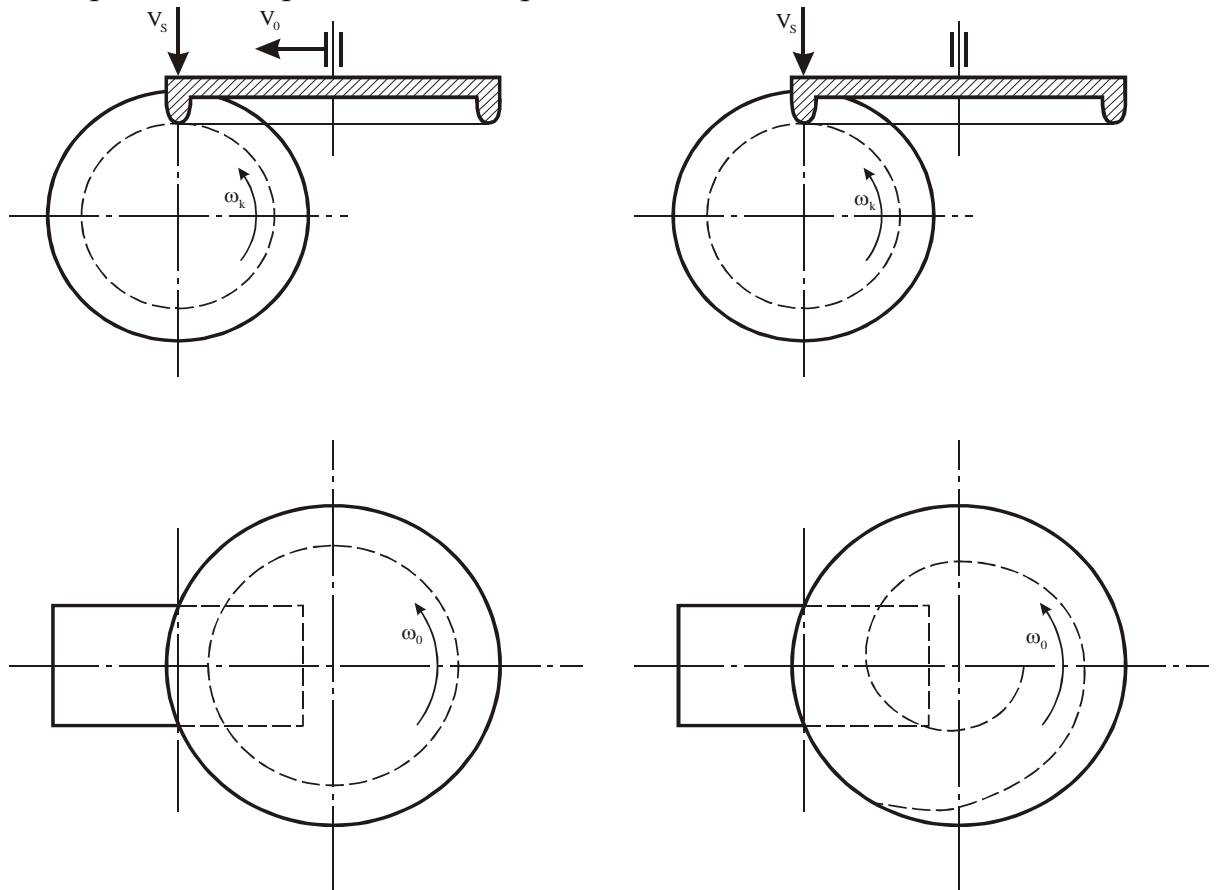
Некоторые геометро-кинематические схемы обработки арочных зубьев.
